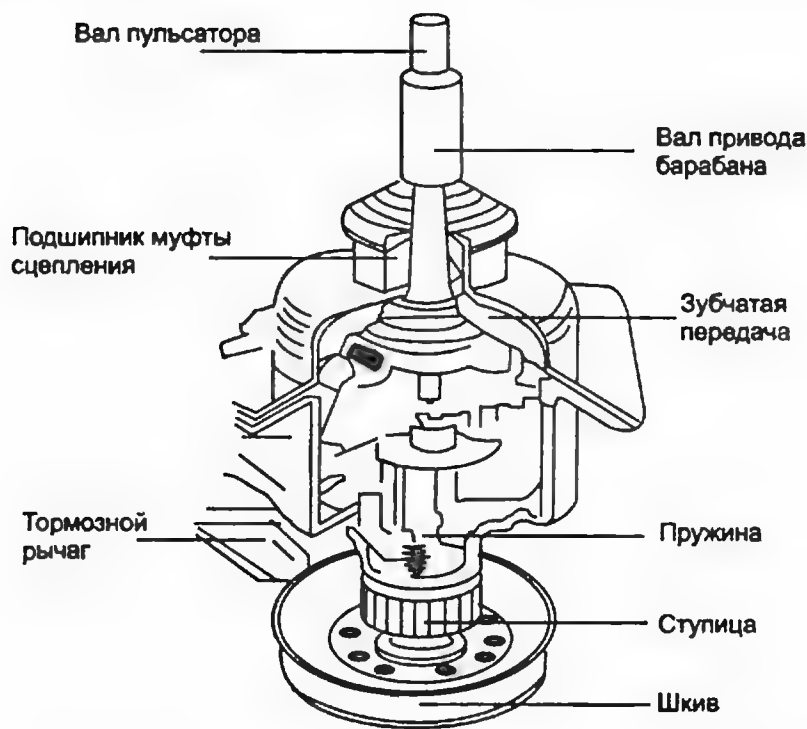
Устройство механизма передачи (редуктора)
